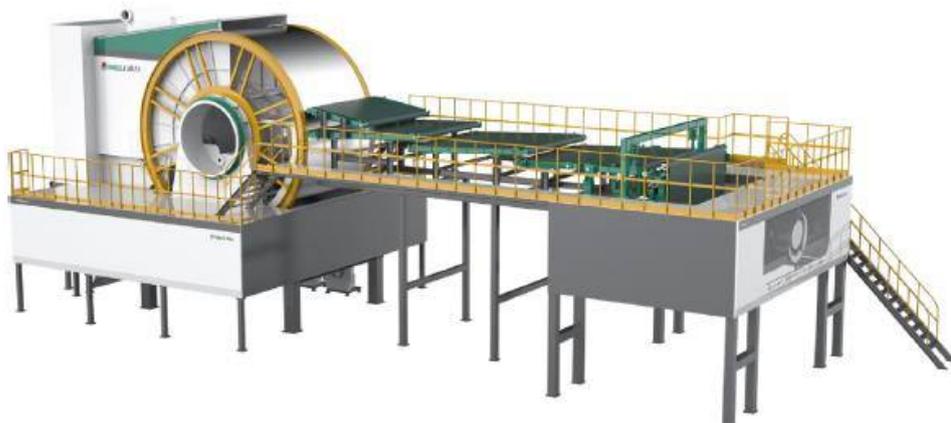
Внешний вид машины для сбора ваты, конвейера для сбора нитей и маятника
